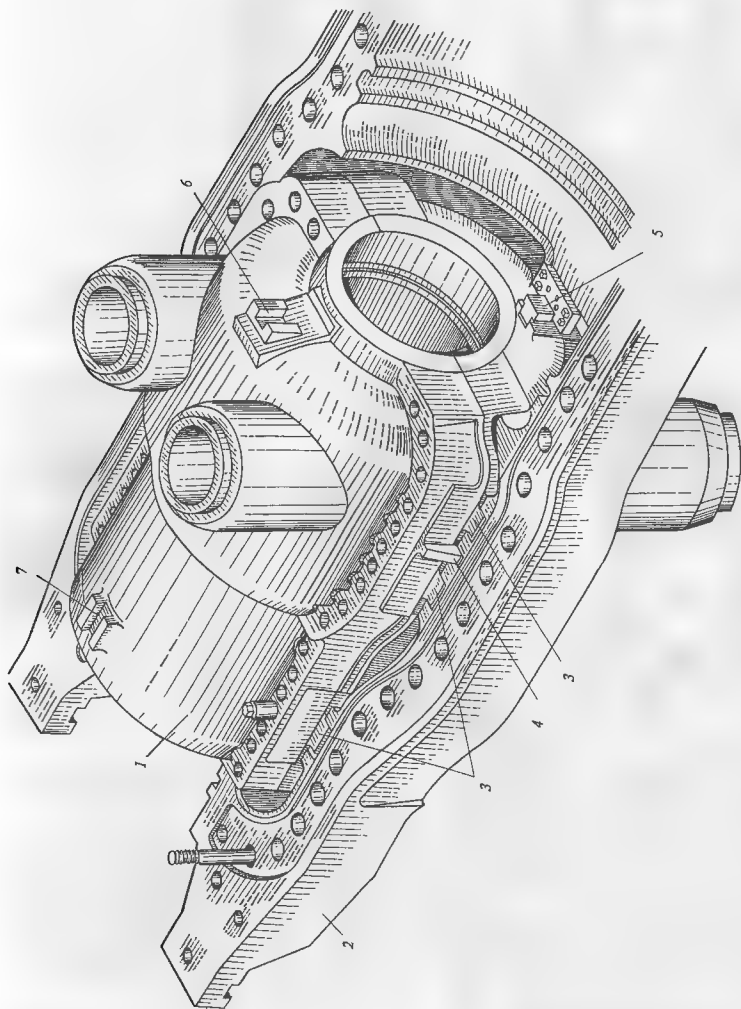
Установка внутреннего корпуса двухступенного цилиндра во внешнем корпусе
